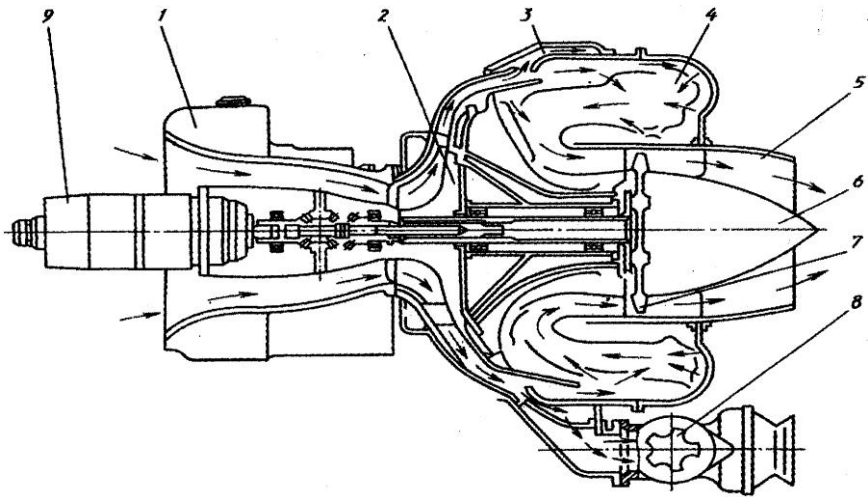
Вспомогательный газотурбинный двигатель:
